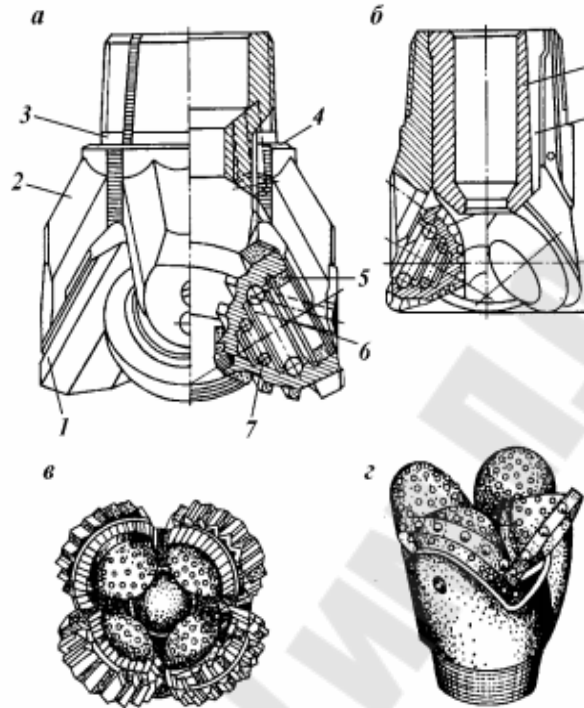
Конструкции четырехшарошечных бурильных головок: а – 1 – шарошка; 2 – лапа; 3 – соединительная головка с конической замковой резьбой; 4 – промывочный узел; 5,6,7 – подшипники (Р-Ш-Ш); б – 1 – внутренний керноприемник; 2 – промывочный канал а) – с внутренним центратором керна; б – с внутренним керноприемником; в – с шарошками, имеющими комбинированное вооружение: наружное скважинообразующее – фрезерованные зубья; внутреннее кернообразующее – твердосплавные, карбидвольфрамовые зубки; г – со сферическими шарошками, имеющими твердосплавное, карбидвольфрамовое вооружение (зубки)
